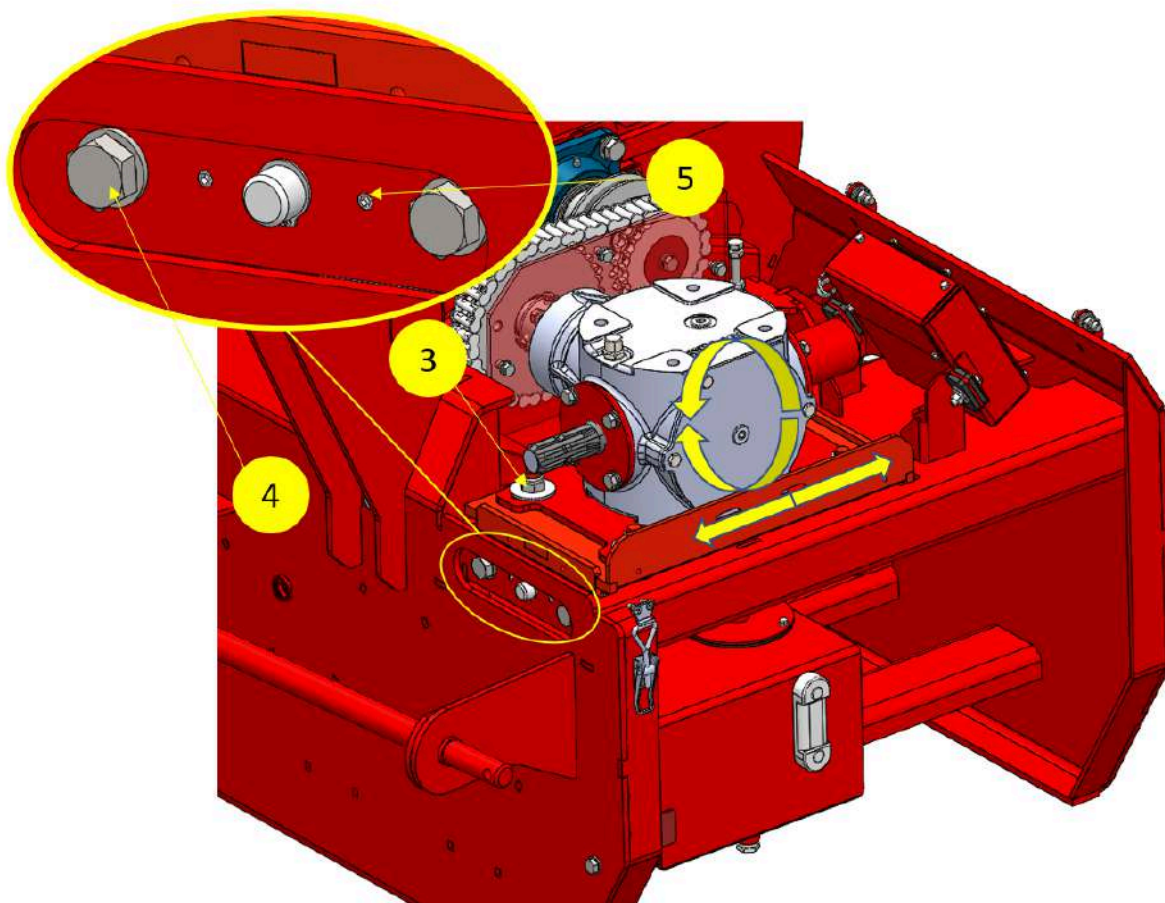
Кріпильні болти регулювальної платформи редуктора: 3, 4, 5 - кріпильні болти платформи
